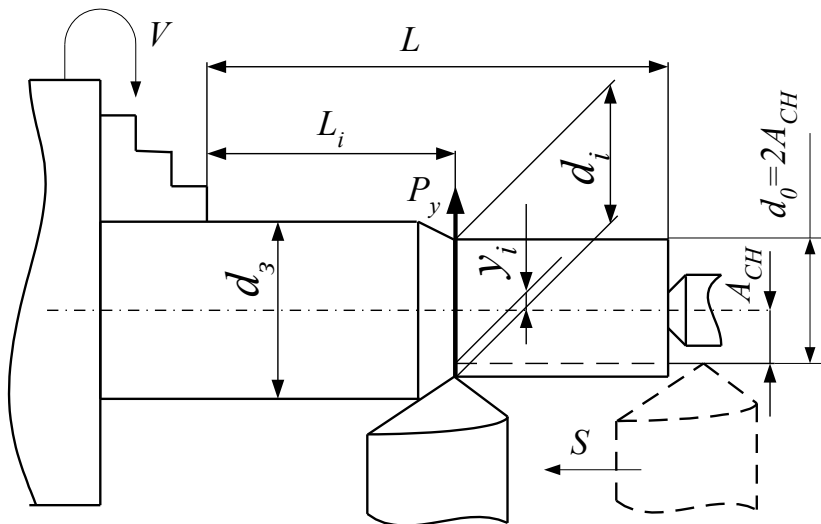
Схема обтачивания вала с установкой заготовки на задний центр
